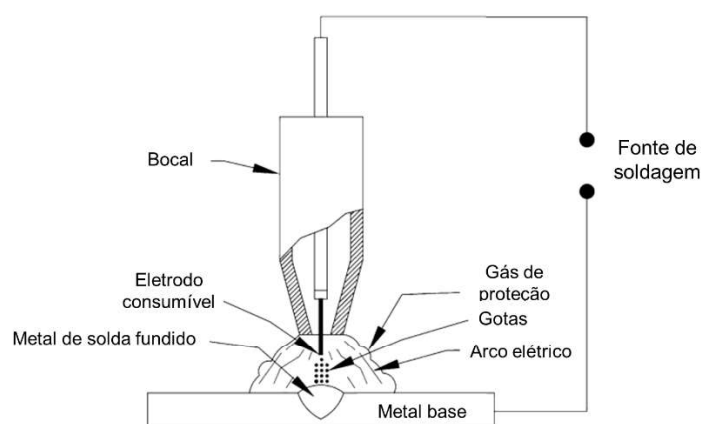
Circuito de soldagem GMAW (Adaptado de PAL; PAL, 2011)
